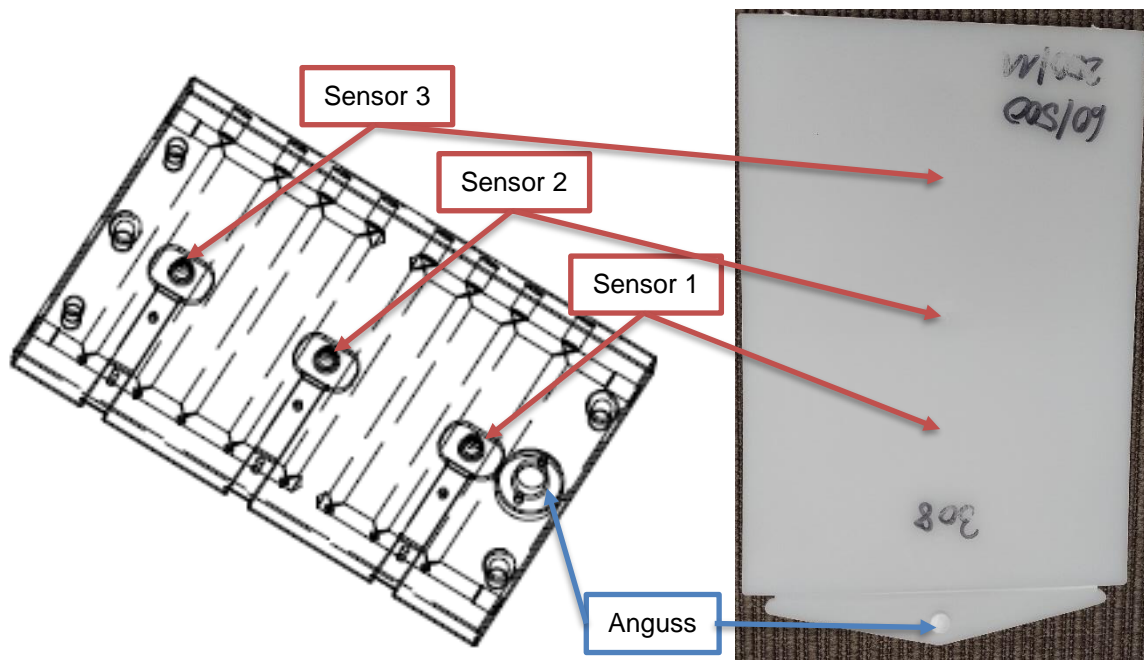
links: Technische Zeichnung der Spritzgussform mit den 3 Sensorpositionen. Rechts Gespritzte PP-Platte aus einer Kampagne.
